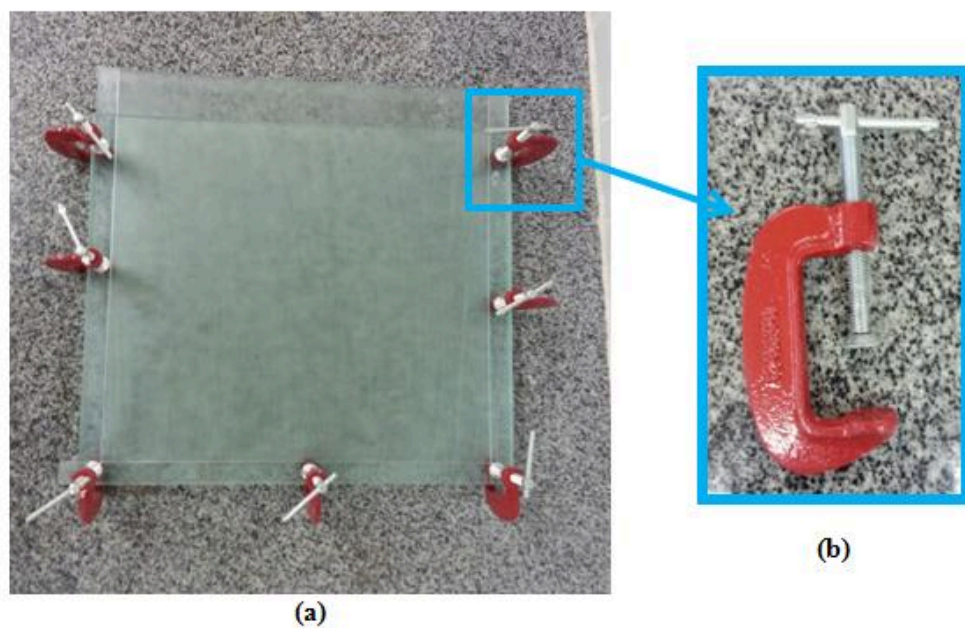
Aplicação do desmoldante (b) no molde de vidro (a).
